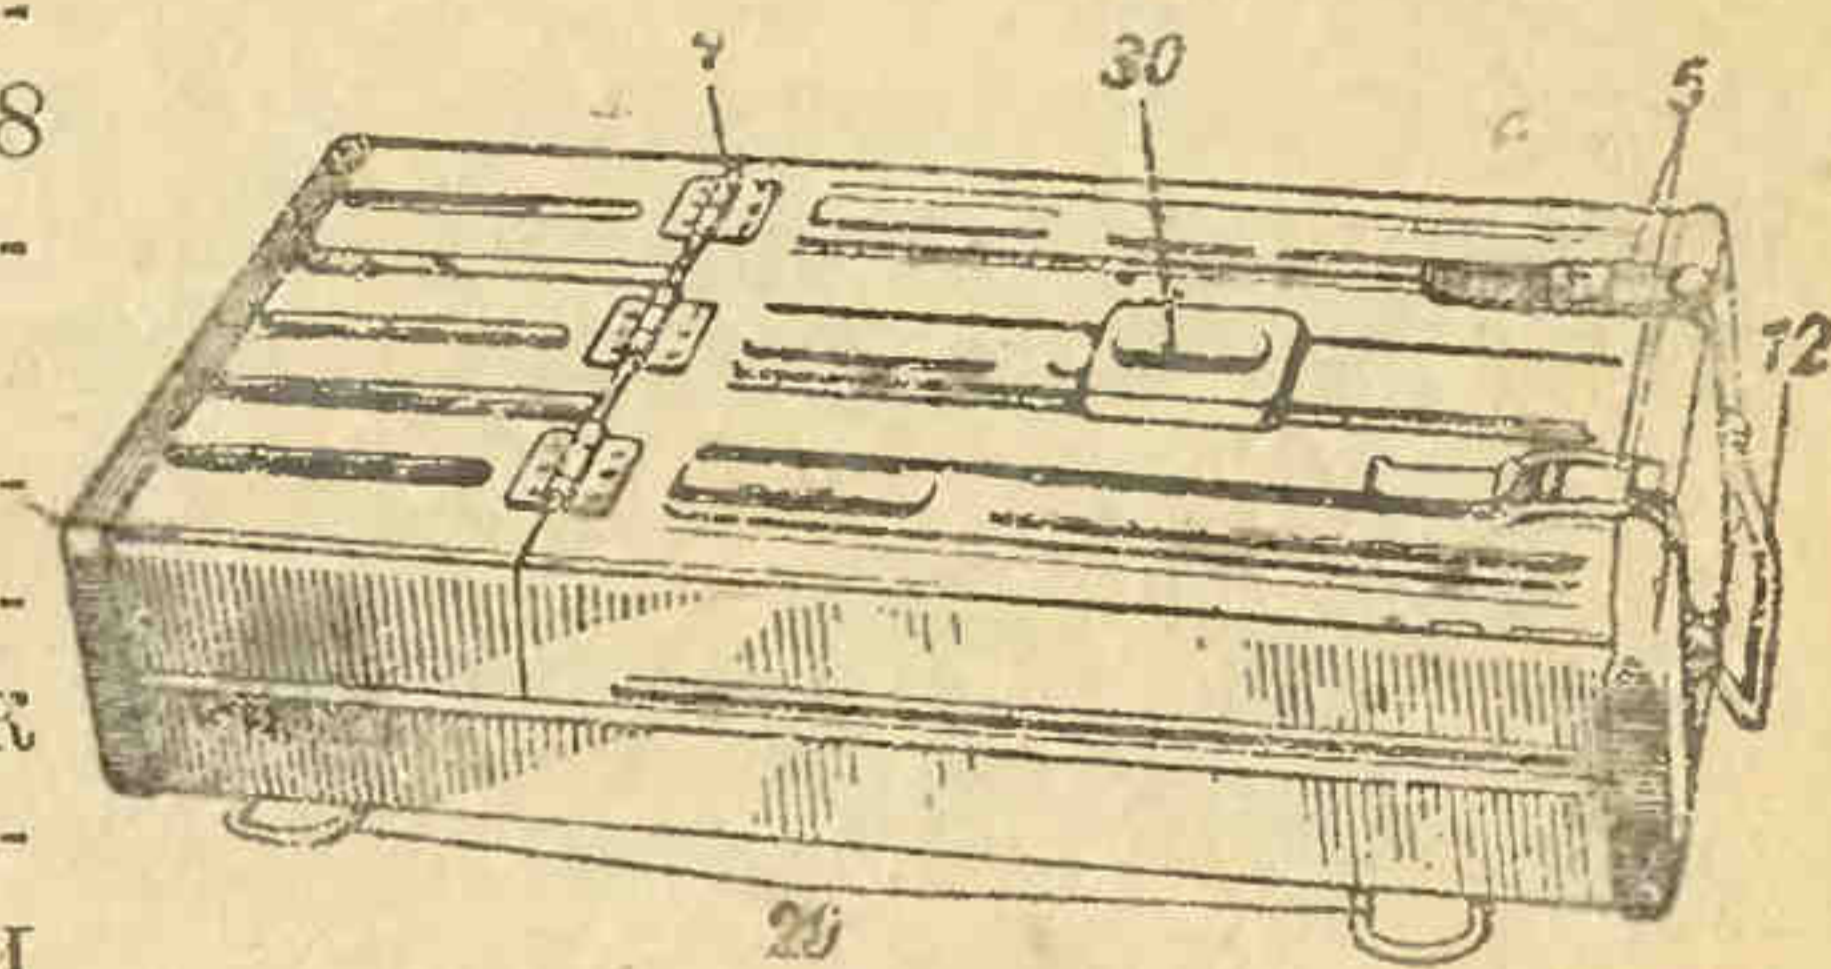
Лоток (сб. 7), общий вид: 4 — петля (сб. 07-1); 5 — замок (сб. 07-6); 12 — ручка (07-18); 20 — скобы (07-32); 30 — упор (07-16).
